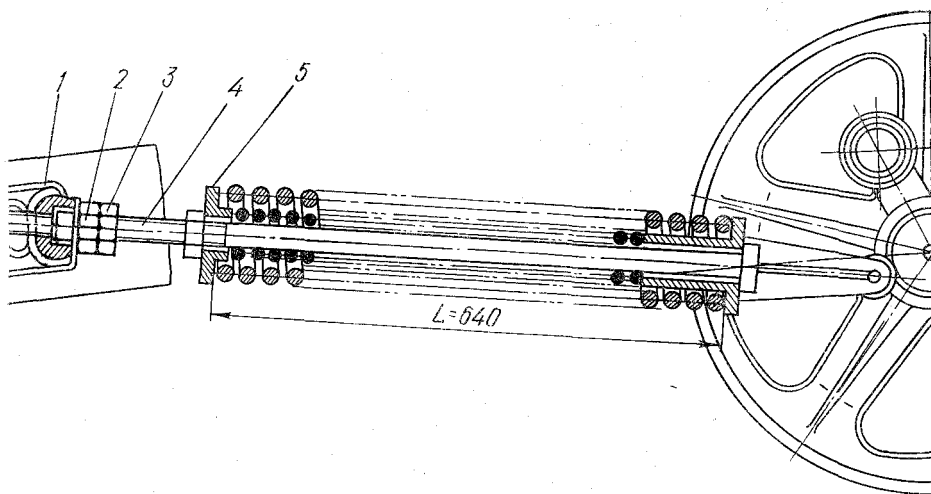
Натяжний пристрій гусениці трактора DT-75M:
